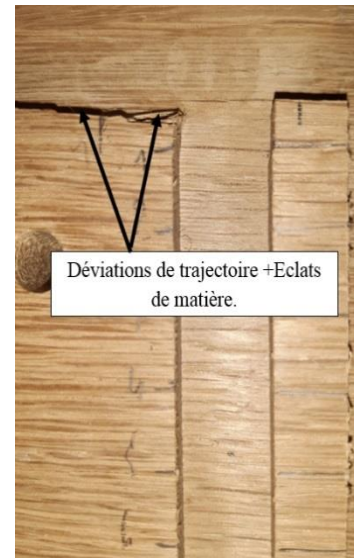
Dégradation d'usinage robotisé du chêne (9000 mm/min)
